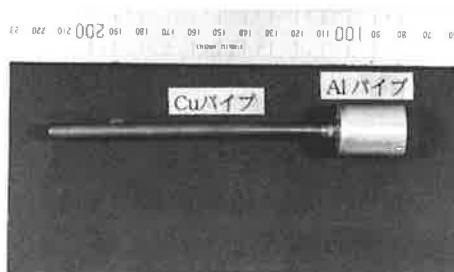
アルミニウムパイプと銅パイプの溶接施工例
